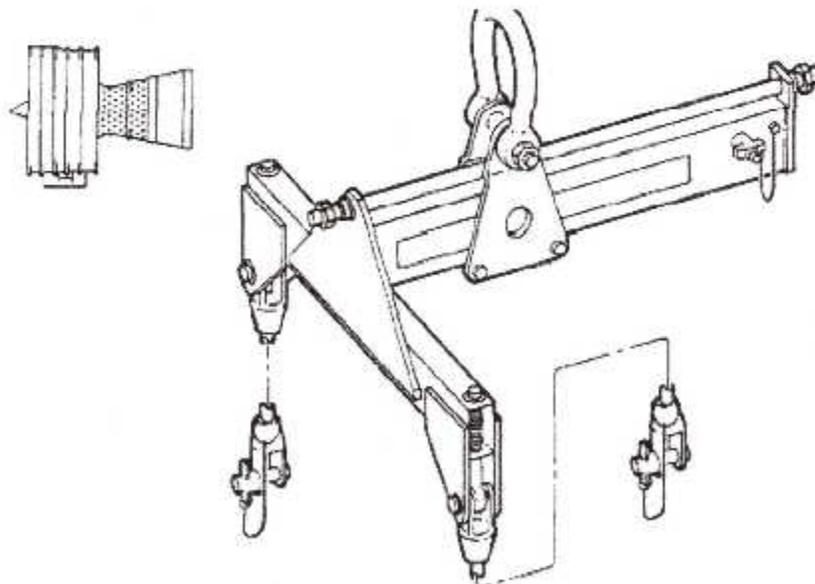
la Poutre de Levage, 856A1107G07.
